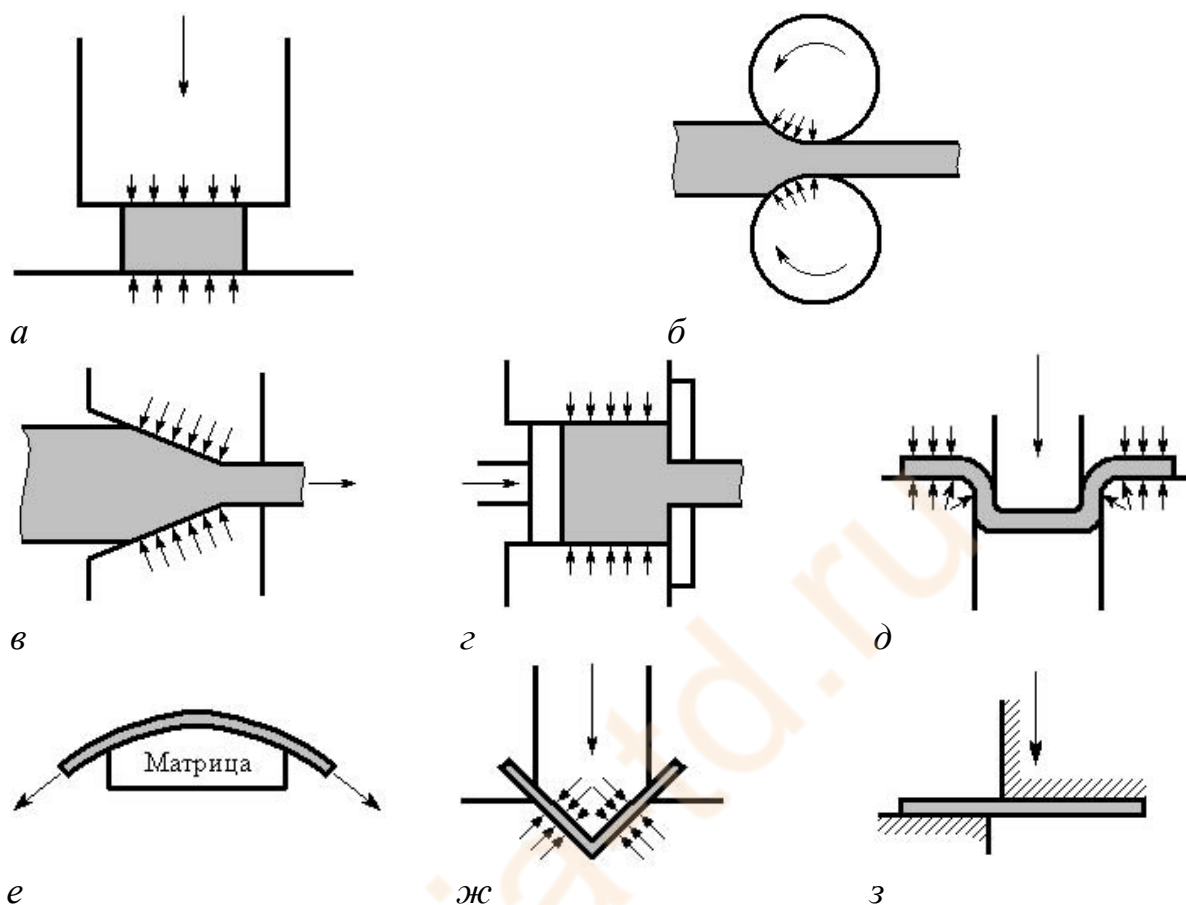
Основные технологические схемы обработки металлов давлением: а – осадка; б – прокатка; в – волочение; г – выдавливание; д – вытяжка; е – протяжка; ж – гибка; з – вырубка
